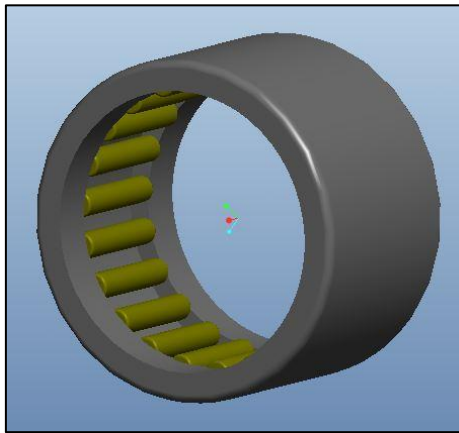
Rodamiento HK 2520 2RS en Pro Engineer.
